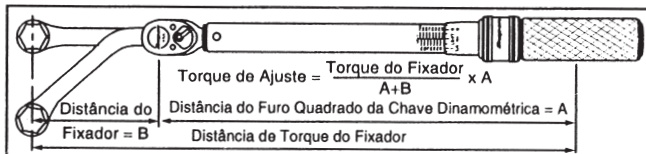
O torque do fixador é maior do que o torque do furo quadrado da chave dinamométrica.
